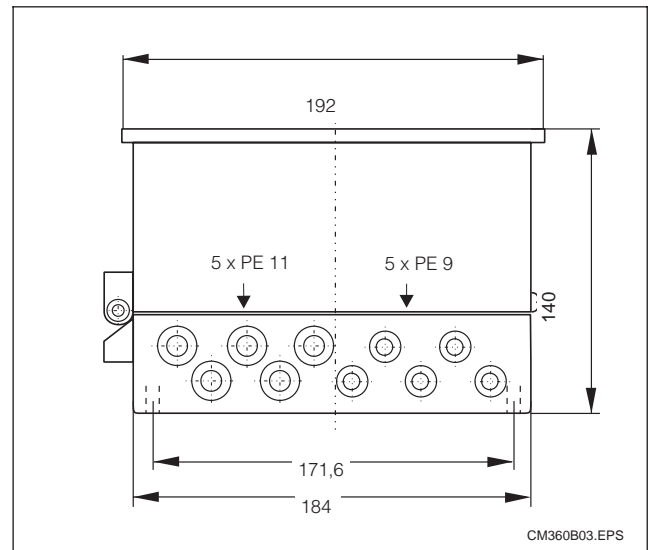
PoolPac, dimensions de l'appareil et vue du dessous
